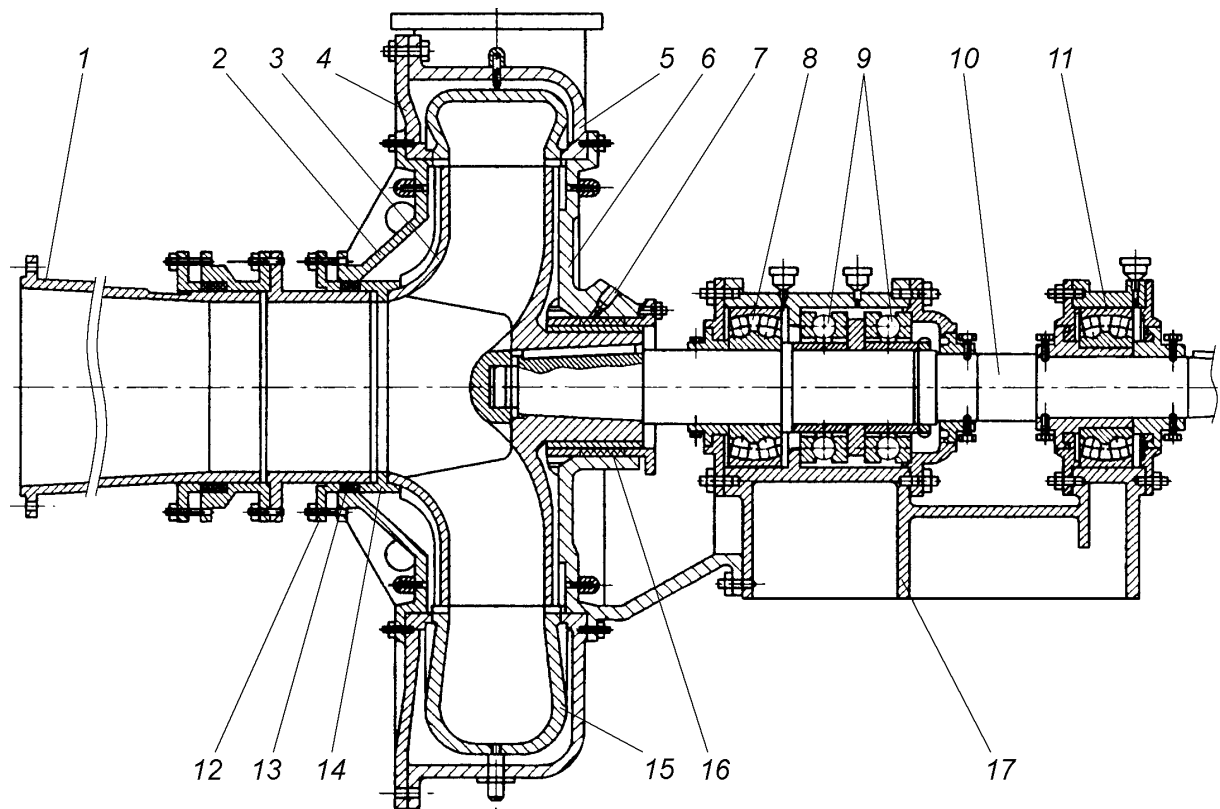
Грунтовий насос типу *МП*: 1 – усмоктувальний патрубков; 2 – передня кришка; 3 – робоче колесо; 4 – кришка для заміни броне-вкладиша; 5 – зовнішній корпус; 6 – задня кришка; 7 – штуцер подачі віджимної води; 8 – передній роликопідшипник; 9 – здвоєний упорний шарикопідшипник; 10 – вал; 11 – задній роликопідшипник; 12 – сальникова кришка; 13 – гумові ущільнювальні кільця; 14 – комір; 15 – внутрішній корпус (броневкладиш); 16 – сальник; 17 – станина
